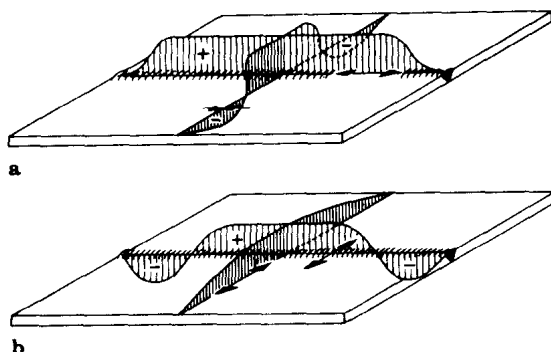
焊接的内应力. a. 沿焊缝方向(纵向应力);
